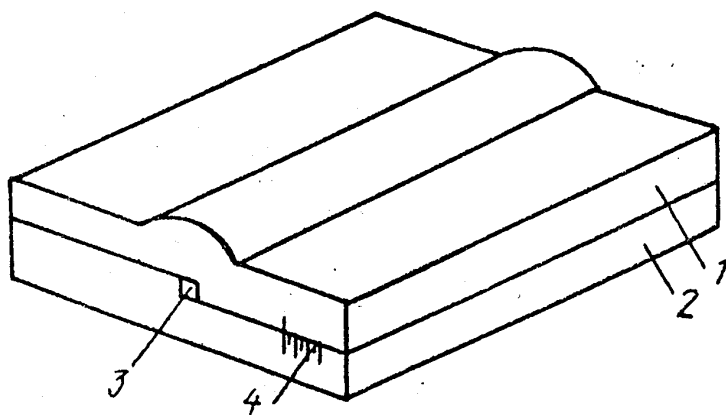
Контрольный образец – имитатор сварного соединения
